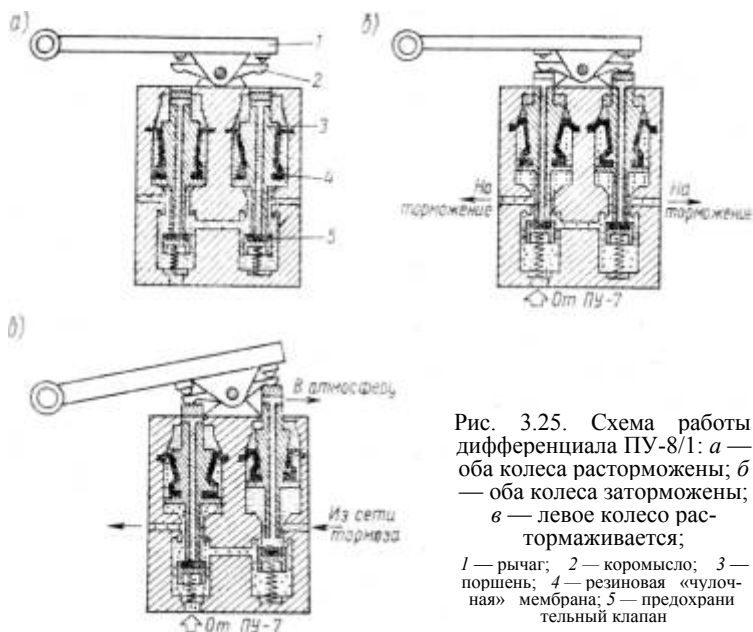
Схема работы дифференциала ПУ-8/1: а — оба колеса расторможены; б — оба колеса заторможены; в — левое колесо растормаживается;
